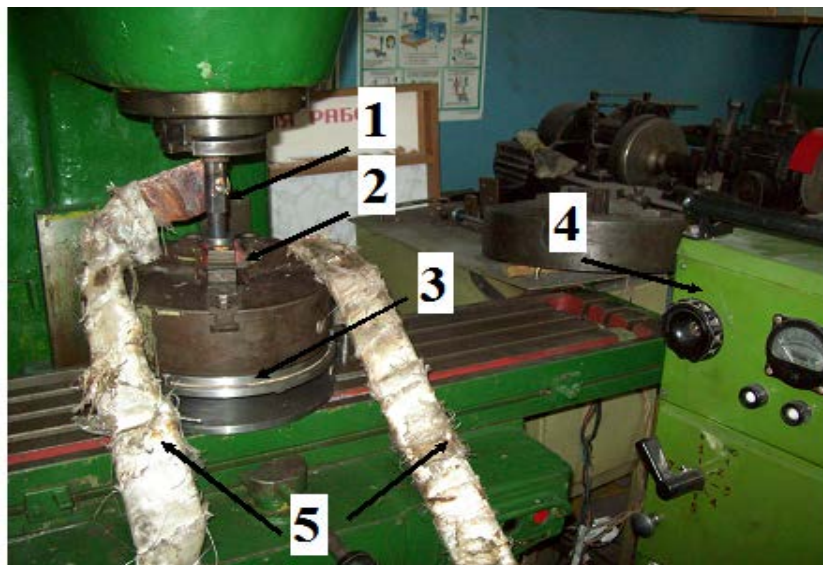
Установка для ПЭМД отверстия колесного цилиндра заднего тормоза автомобиля УАЗ: 1 - инструментальная державка с твердосплавным дорном; 2 – фрагмент тормозного цилиндра; 3 – стол с плавающей платформой; 4 – силовой модуль; 5 – токоподводящие кабели
